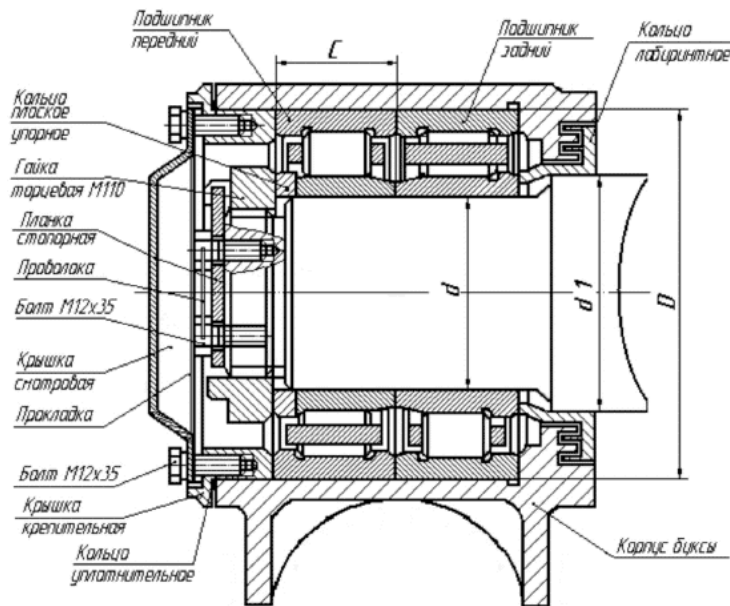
Буксовый узел с двумя подшипниками роликовыми цилиндрическими с торцевым креплением гайкой М110
